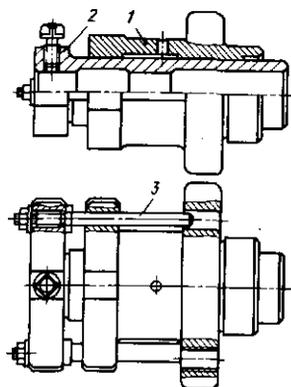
Приспособление для крепления резьбонарезных головок: 1 — корпус; 2 — пиньоль для крепления резьбонарезных головок; 3 — скалка
